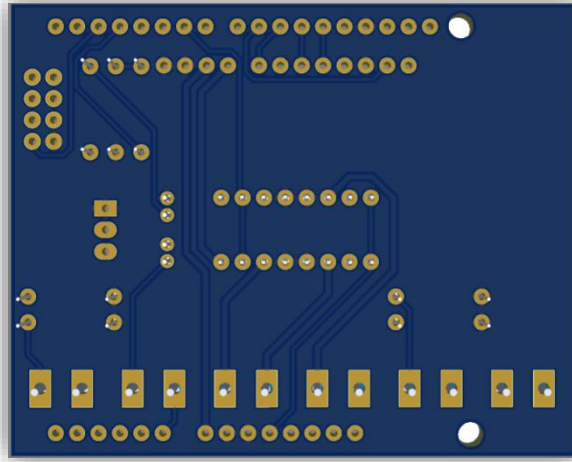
Diseño capa inferior PCB, Proteus 8 Profesional - LockBikeRack
